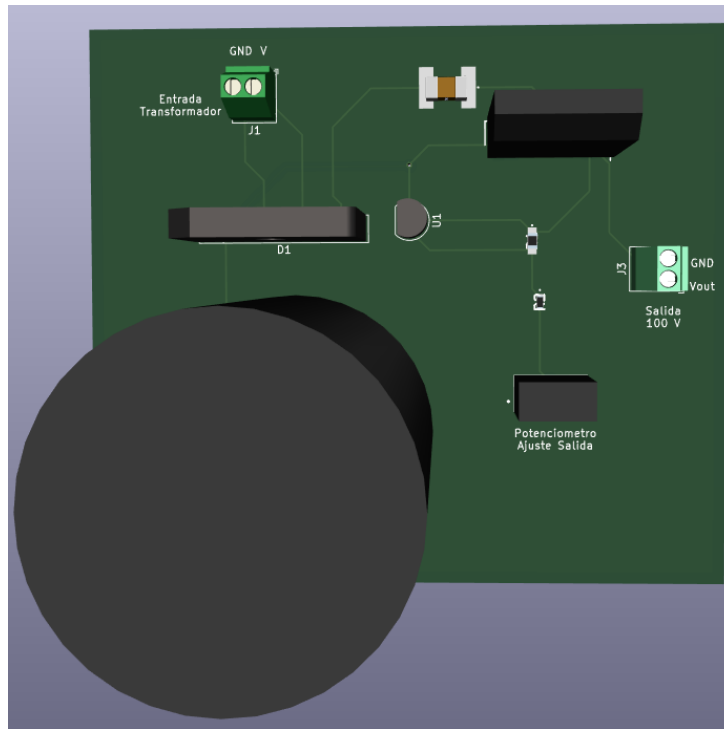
Resultado 3D de la PCB de la fuente de 100 V.
